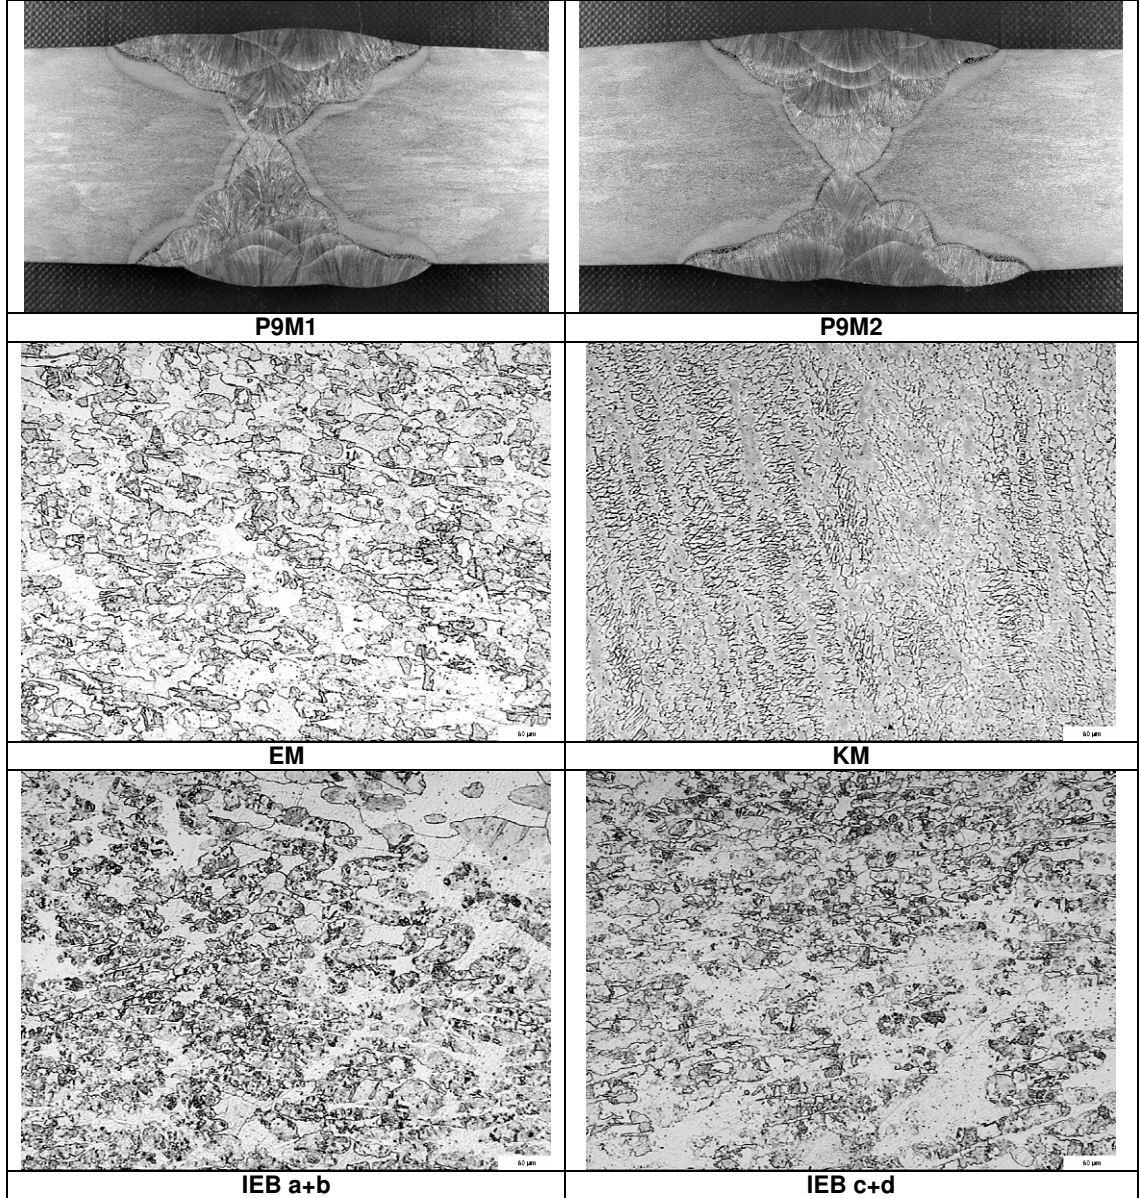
20 mm kalınlığında 309 tür ek metal ile SAW kaynaklı bağlantının makro ve mikroyapıları (A9).
